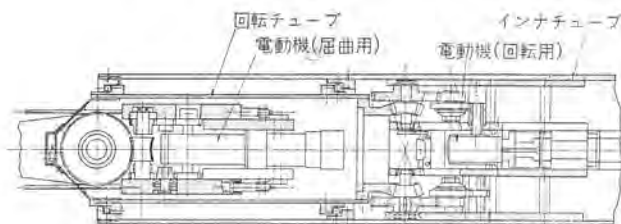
肩 Fig. 3.5 Shoulder assembly.
